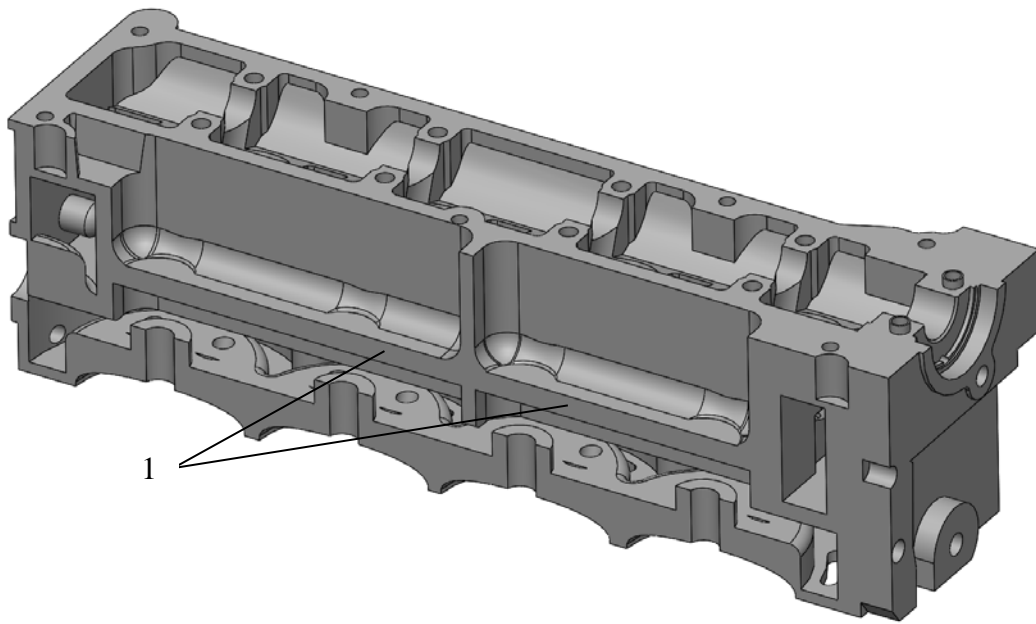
Vista em corte do cabeçote após terceiro passo de fabricação.
